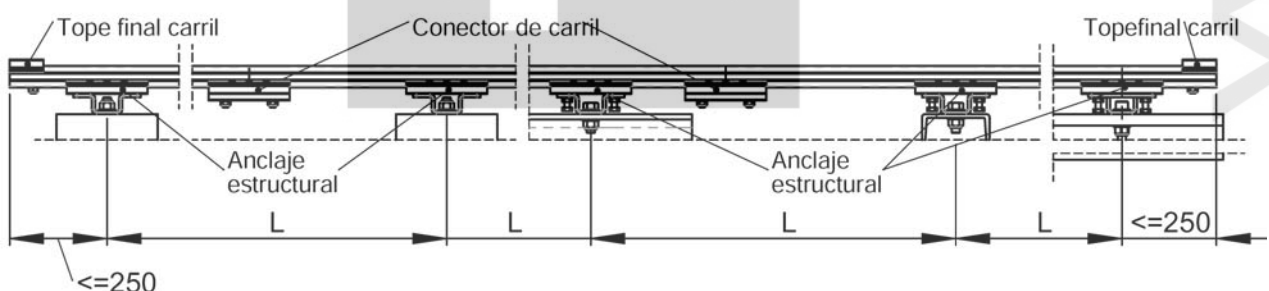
Método de instalación "anclaje estructural desplazado"
